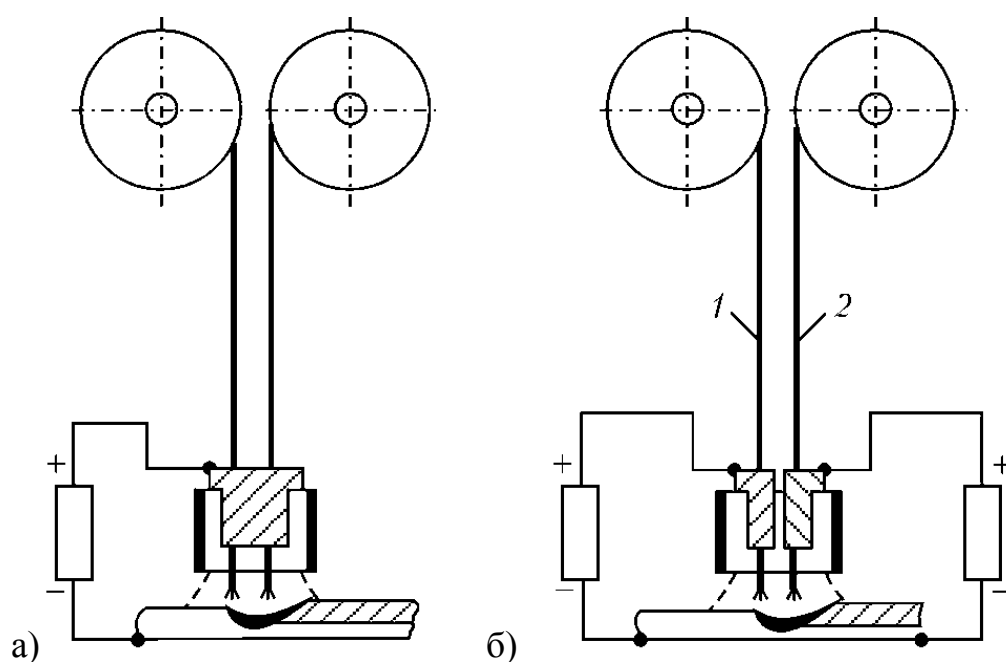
Существующие схемы сварки: а) сварка расщеплённым электродом; б) сварка двумя дугами
